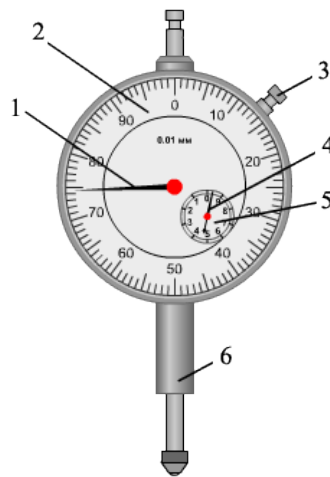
Індикатор годинникового типу: 1 – велика стрілка; 2 – шкала індикатора; 3 – стопор; 4 – стрілка; 5 – відлікова шкала; 6 – вимірювальний стрижень
